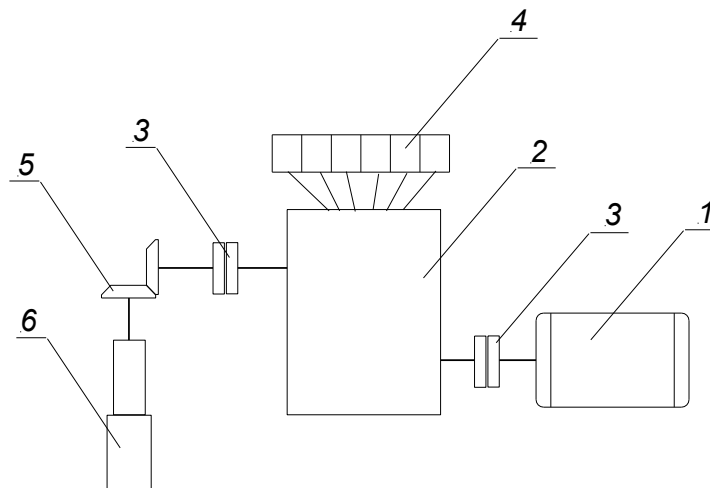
Принципова схема привода головного руху фрезерувального верстата МА655А7
